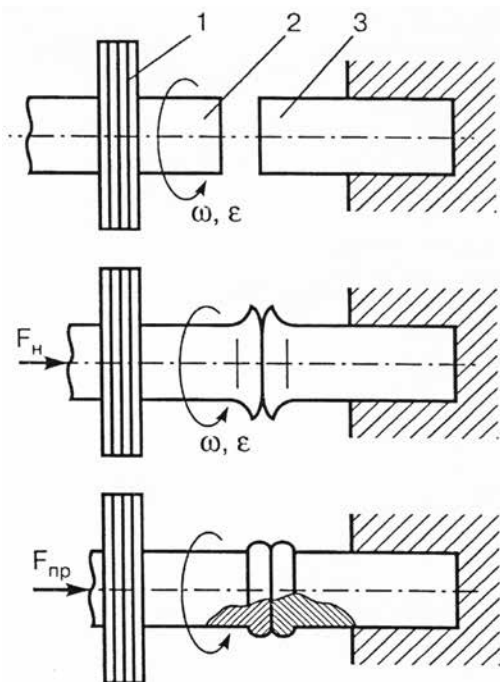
Схема инерционной сварки трением: 1 – маховик; 2, 3 – свариваемые заготовки
